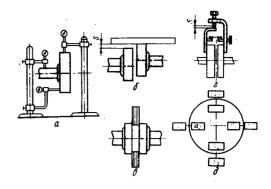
Схема проверки положения машин при муфтовом сцеплении:
